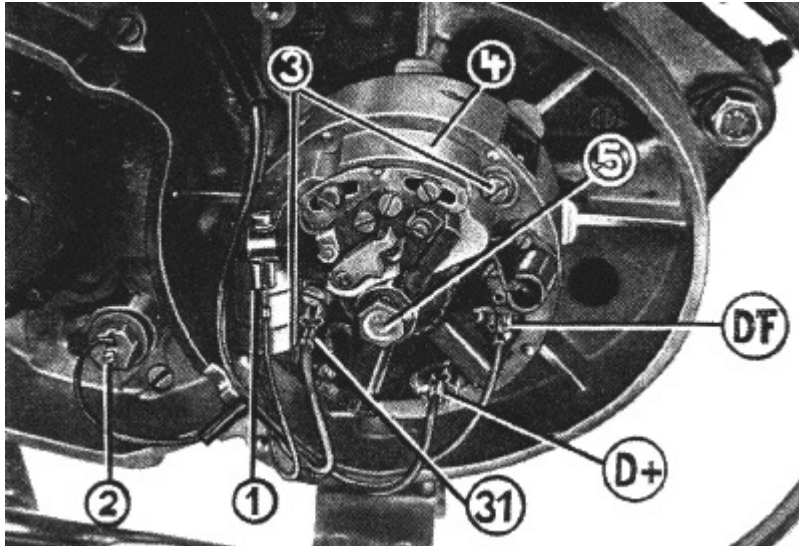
Ausbau der Haltekappe der Lichtmaschine
